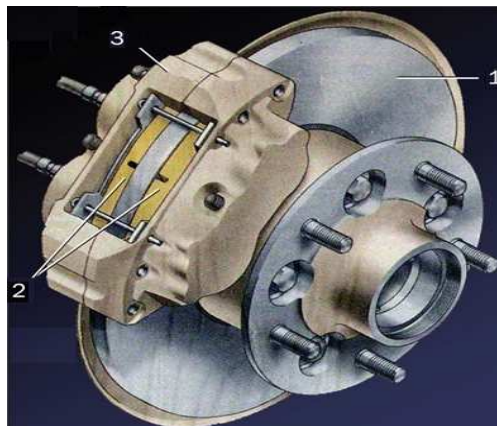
Дисково-колодочный тормоз: 1 – вращающийся сплошной тормозной диск; 2 – неподвижные колодки с фрикционными накладками; 3 – суппорт
